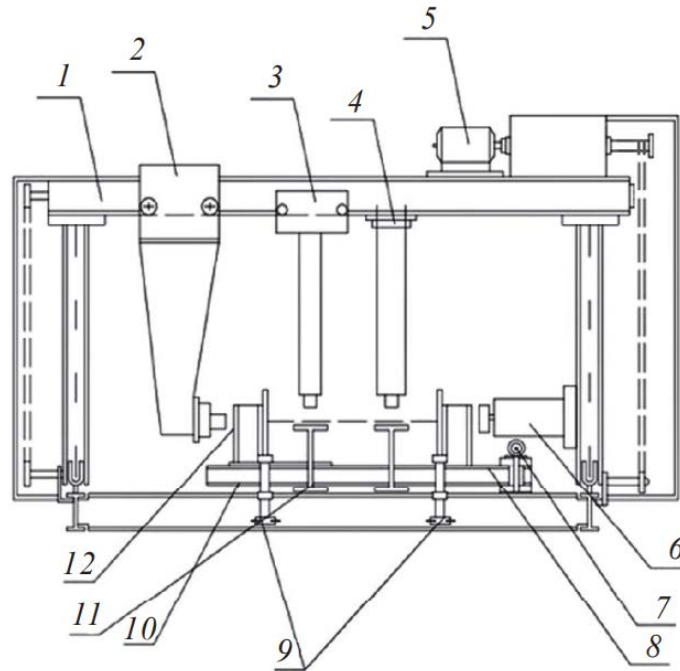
Установка з рухомим порталом для складання стрижнів двотаврового перерізу: 1 - портал; 2,3 - рухомі пневмопритискувачі; 4,6 - нерухомі пневмопритискувачі; 5 - мотор; 7 - привідний вал; 8, 12 - стійки; 9 - гвинтовий упор; 10 - привідний гвинт переміщення рухомої опори; 11 - рухома опора; 13 - рама
